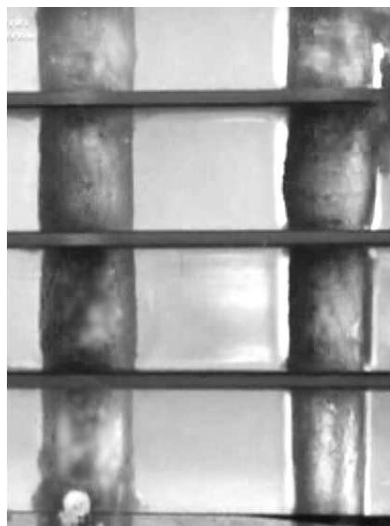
Отверстия, просверленные сверлом с круглой (слева) и конической (справа) режущей частью
